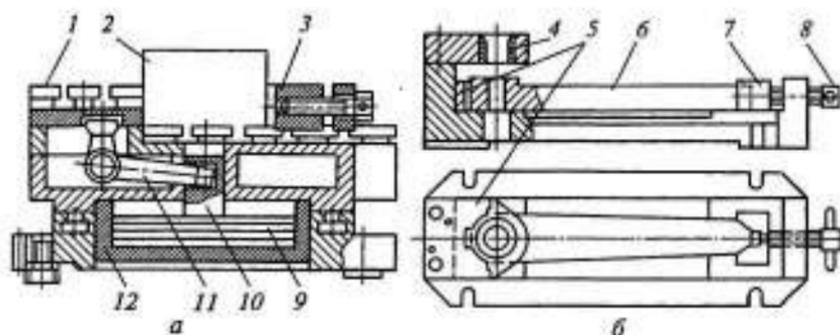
Приспособления для закрепления заготовок при сверлении:
